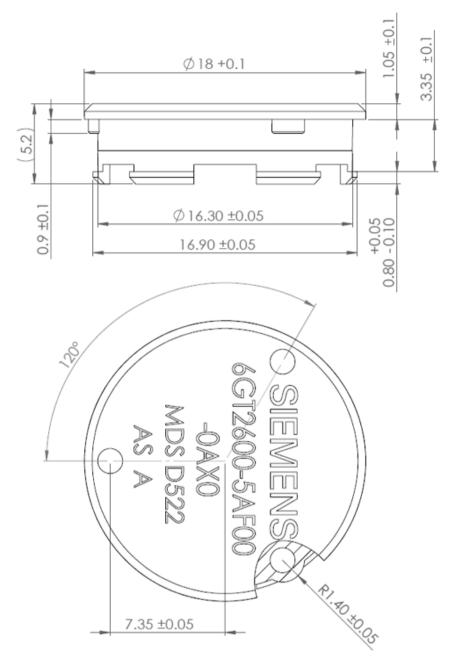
Desenho de dimensões variante especial do MDS D522
